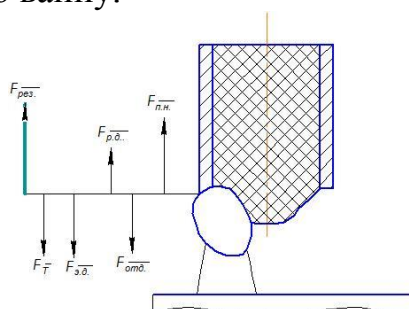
Схема модели при номинальном значении сварочного тока
